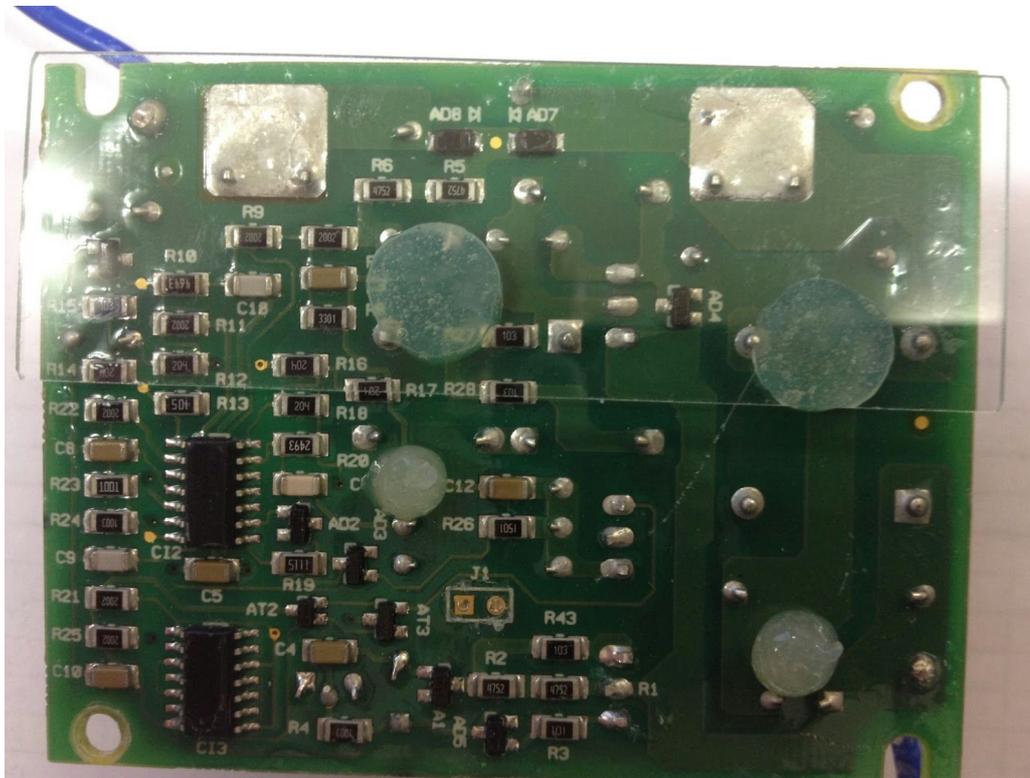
Aplicación de adhesivo para fijar la placa de apantallamiento
